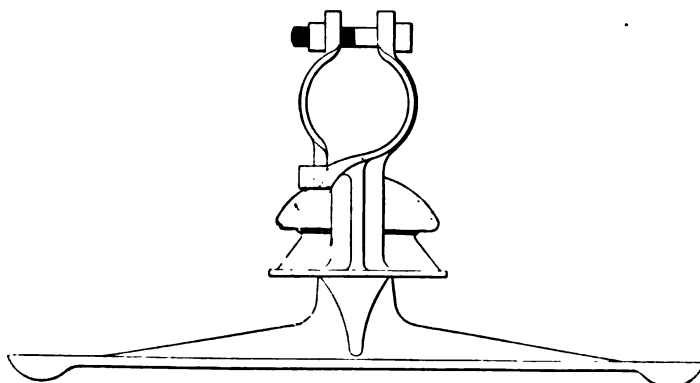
Collier de fixation sur console (vue parallèlement au fil).
